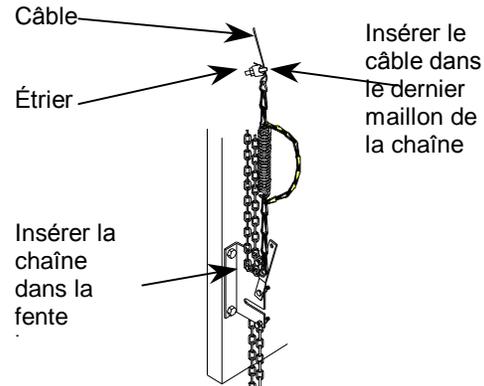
Levier sectionneur pour l'ouvre-porte MSJ
